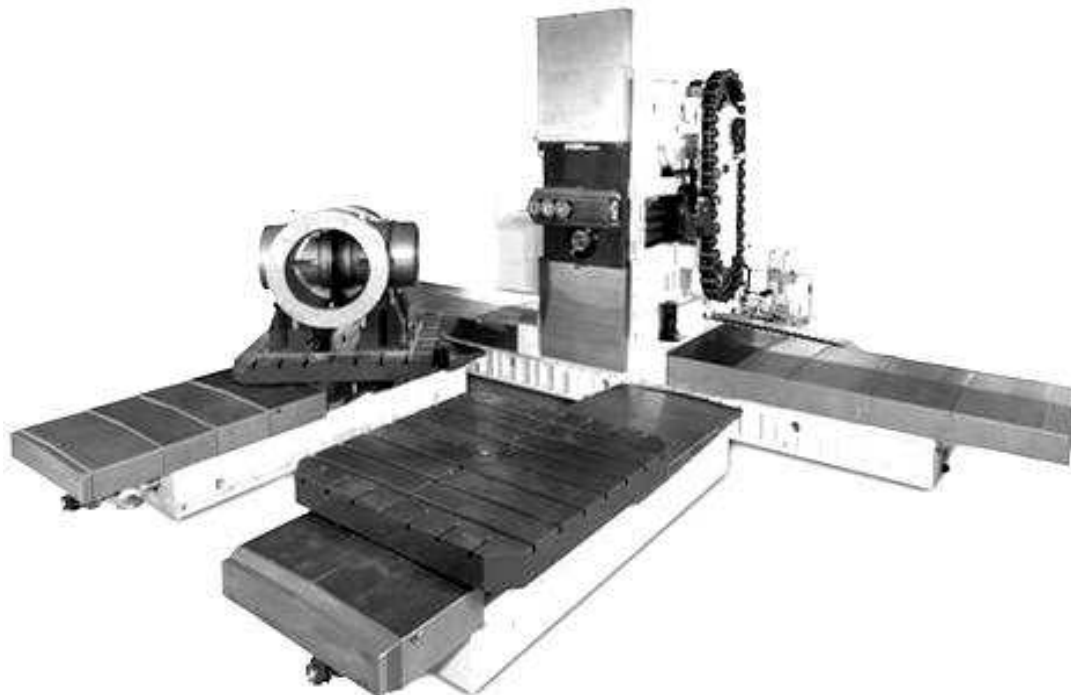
Обрабатывающий центр с ЧПУ Trevisan DS1500/450S
